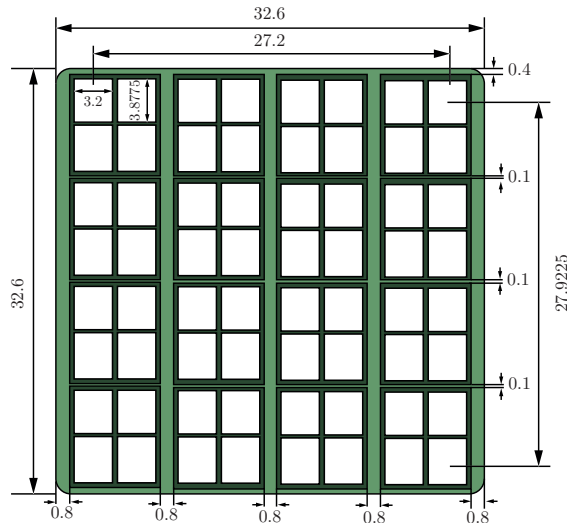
Dimensiones (mm) de la PCB de dSiPMs Philips 3200 22-44.
